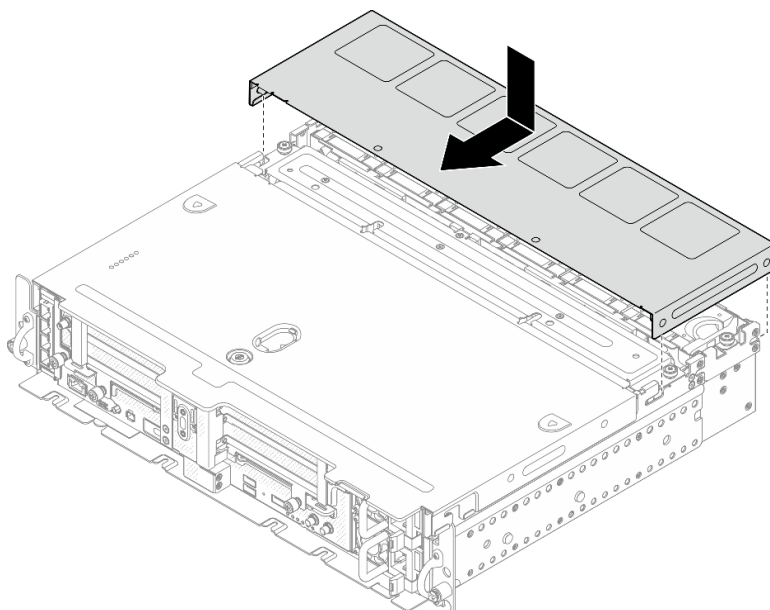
Instalación de la cubierta del ventilador (360 mm)
